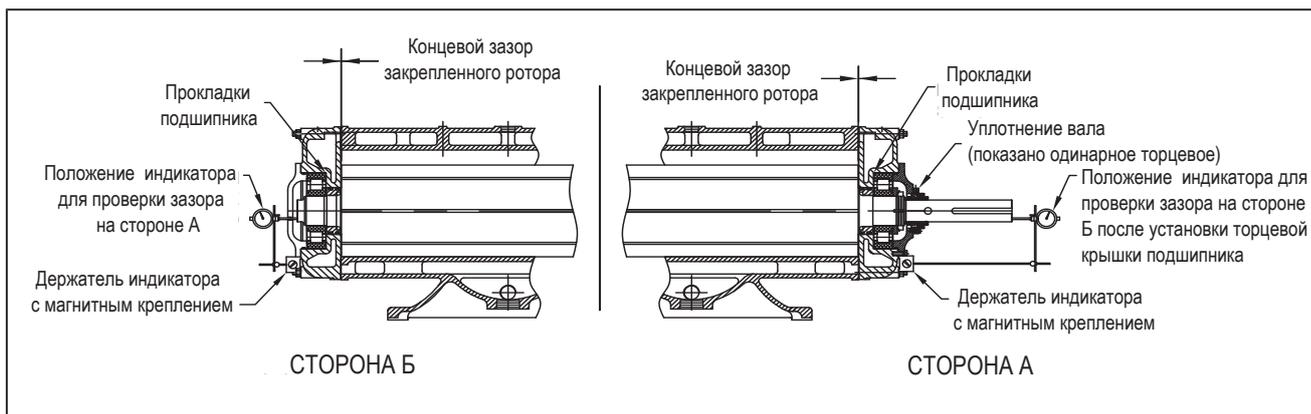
Концевые зазоры ротора. Подшипники установлены на прокладки.
